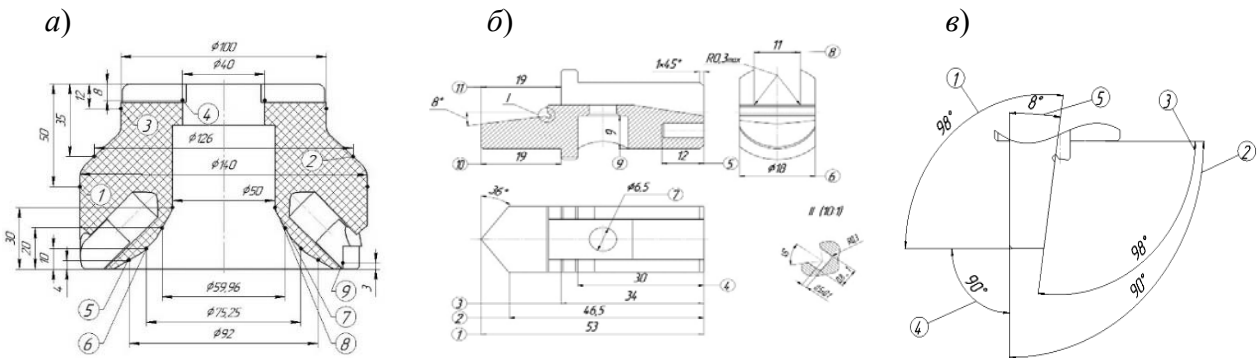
Эскизы: *а* – корпусного модуля; *б* – державки; *в* – измерения угловых параметров
